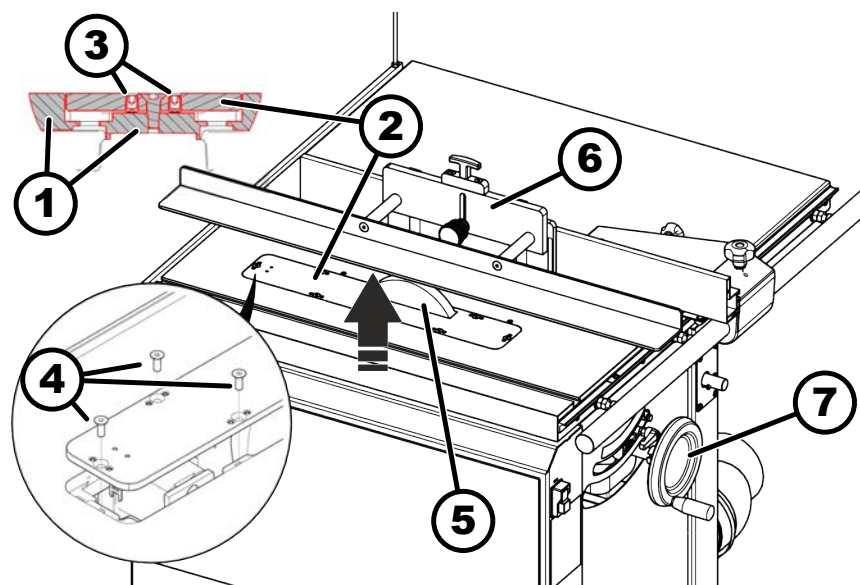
Installer de la planche d'insertion pour les outils de rainurage
